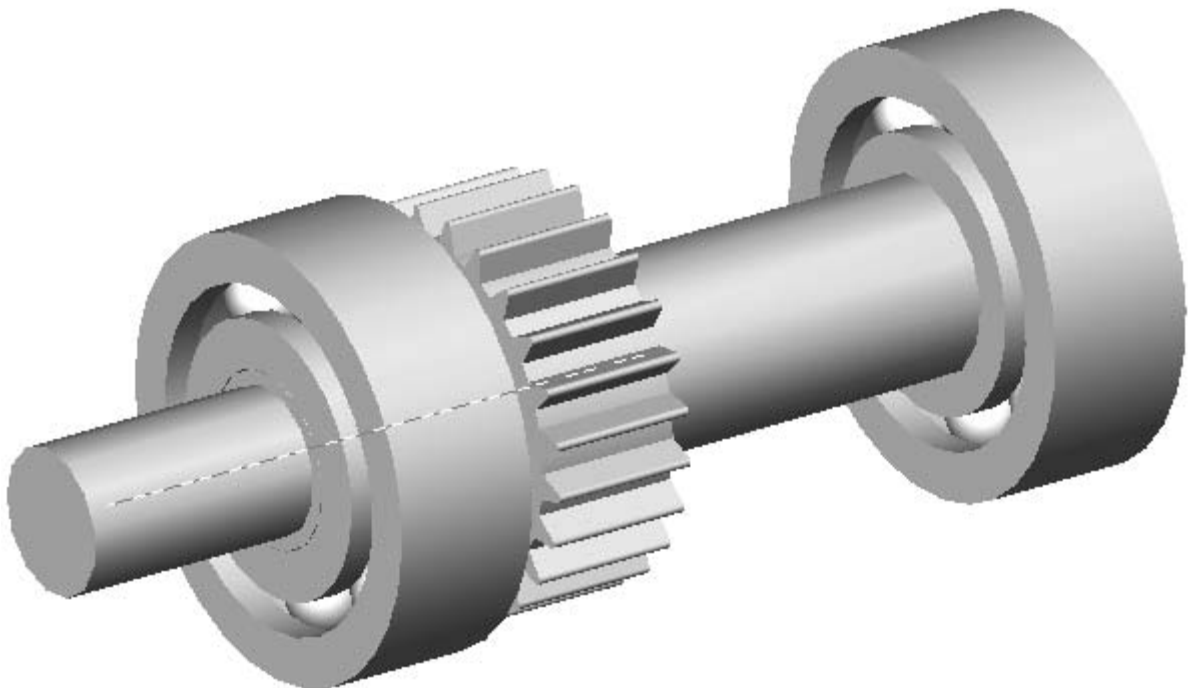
Пример трехмерной модели вала-шестерни в сборе с подшипниками
